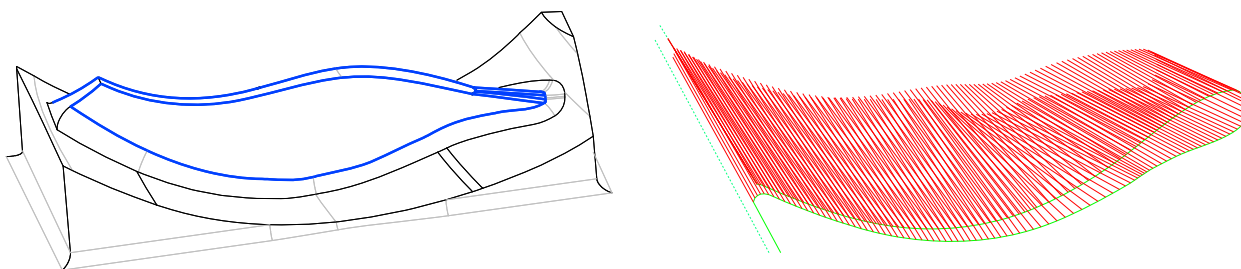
Définition de la surface « impeller » et des trajectoires d'usinage [PECHARD 09]
